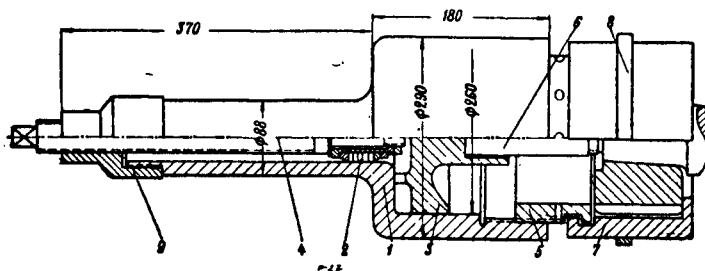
Гидравлический съемник малой шестерни (второй вариант):
